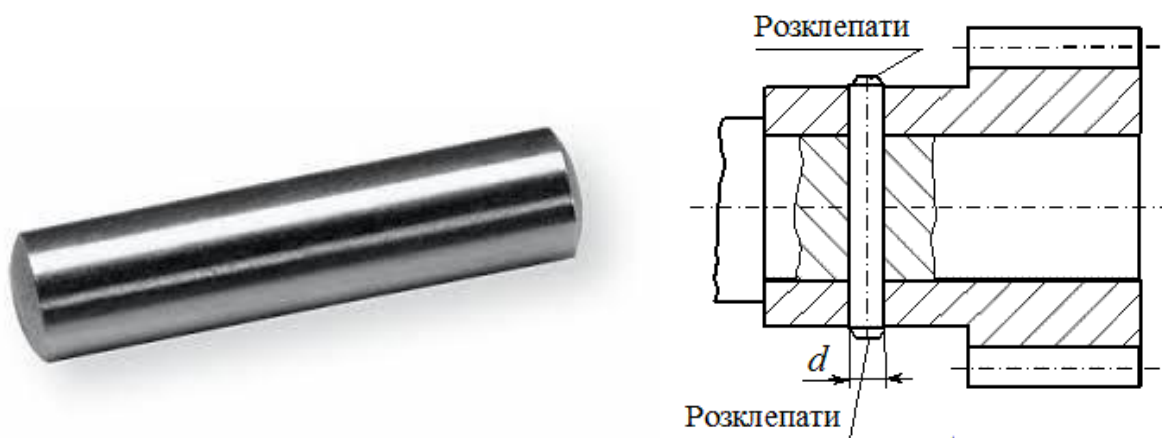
Зовнішній вигляд циліндричного штифта
